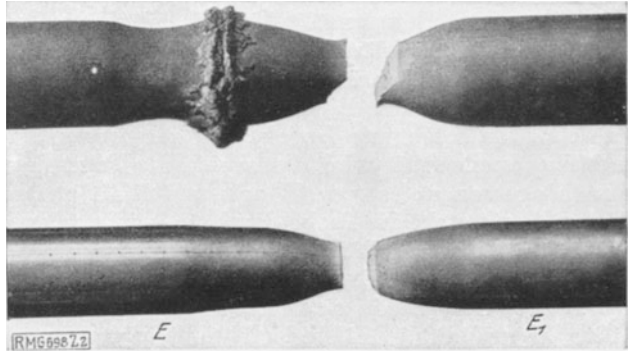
Elektrisch nach dem Abschmelzverfahren geschweißter Probestab, roh und abgedreht zerrissen.
